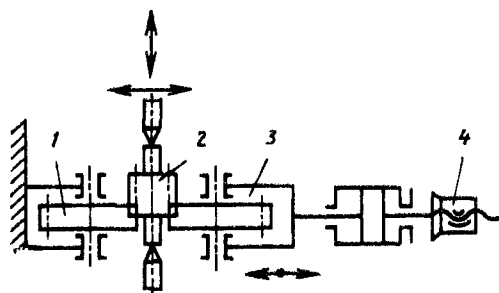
Схема зубокалибровки двумя накатниками с осевым движением подачи инструмента:
